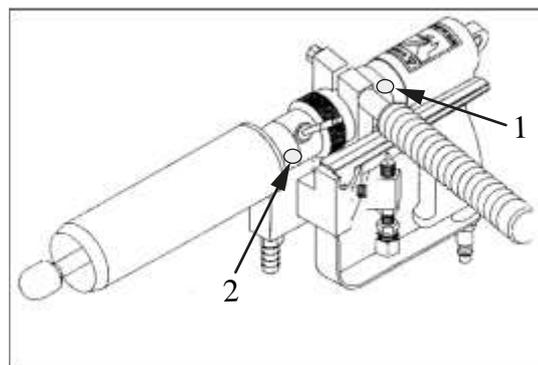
Posición del engrasador de la pieza de mano EDF
